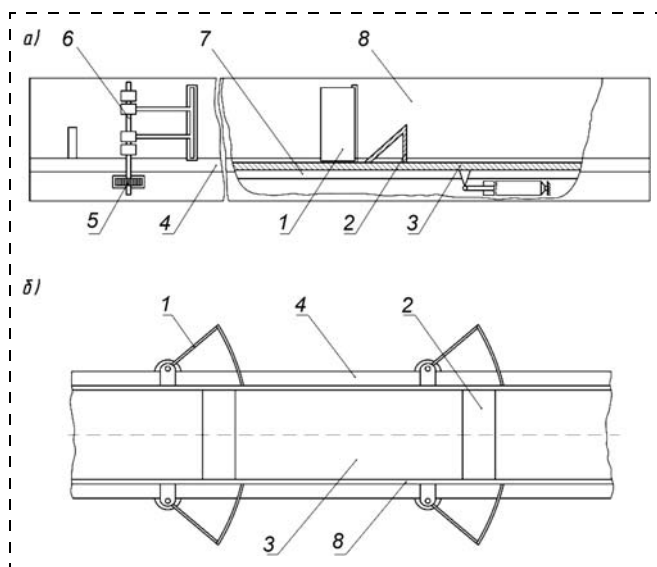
Перегрузатель с изменяемой геометрией неподвижных элементов: а — общий вид перегружателя; б — вид сверху секции перегружателя; 1 — неподвижные ТЭ; 2 — подвижные клиновые ТЭ; 3 — днище; 4 — направляющие; 5 — шестерни; 6 — ось; 7 — зубчатая рейка; 8 — борта
